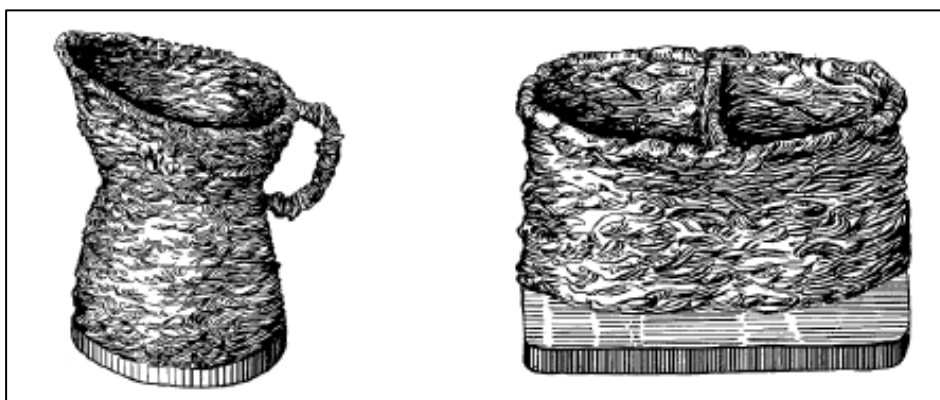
Exemplos de componentes baseados em soldagem 3D criados manualmente por deposição de camadas utilizando processo de soldagem a arco eléctrico e eletrodo revestido [1,17].
